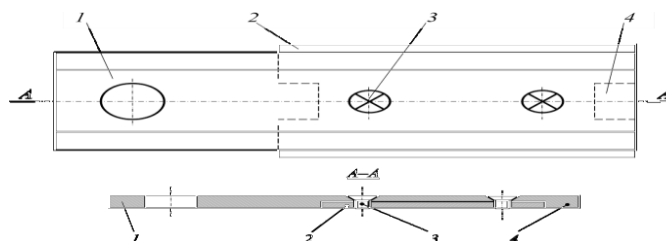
Ніж роторної косарки з нерухомою ріжучою накладкою: 1 – основа; 2 – ріжуча накладка; 3 – гвинти; 4 – виступи
